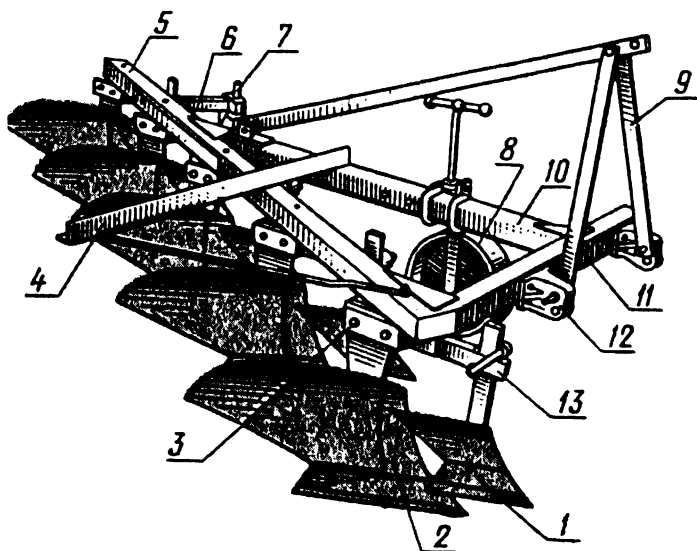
Навесной плуг ПЛН-5-35: 1 — предплужник; 2 — корпус; 3 — угольник; 4 — прицепка для борон; 5 — главная балка; 6 — кронштейн крепления ножа; 7 — дисковый нож; 8 — опорное колесо; 9 — навеска; 10 — продольная балка; 11 — поперечная балка; 12 — кронштейн; 13 — кронштейн предплужника
